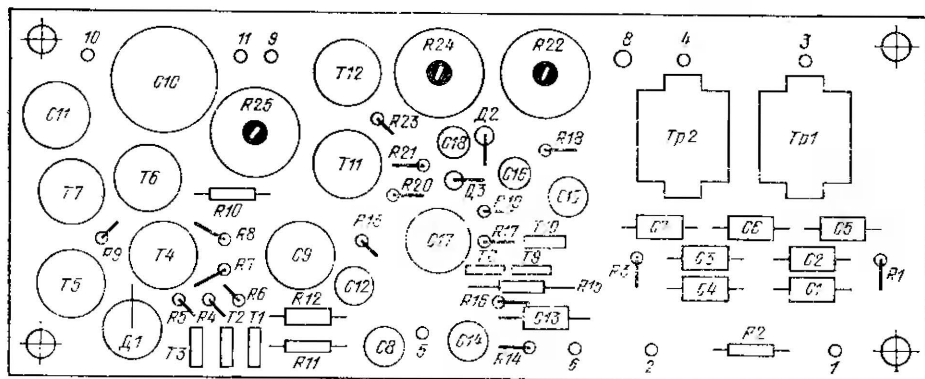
Монтажная схема платы усилителя НЧ-APU (вид сверху)
